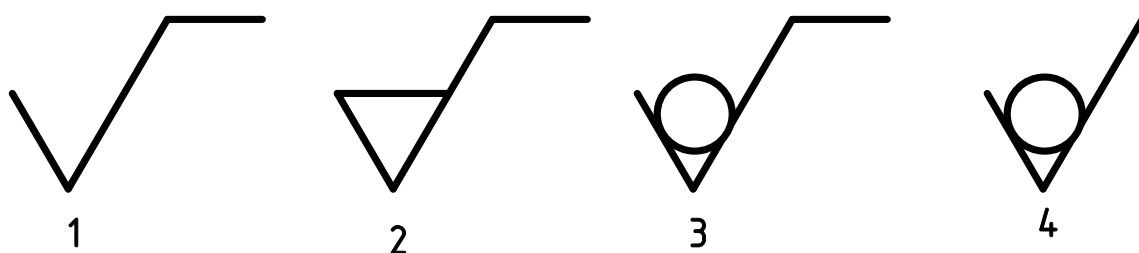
Знаки обозначения шероховатости поверхности:
